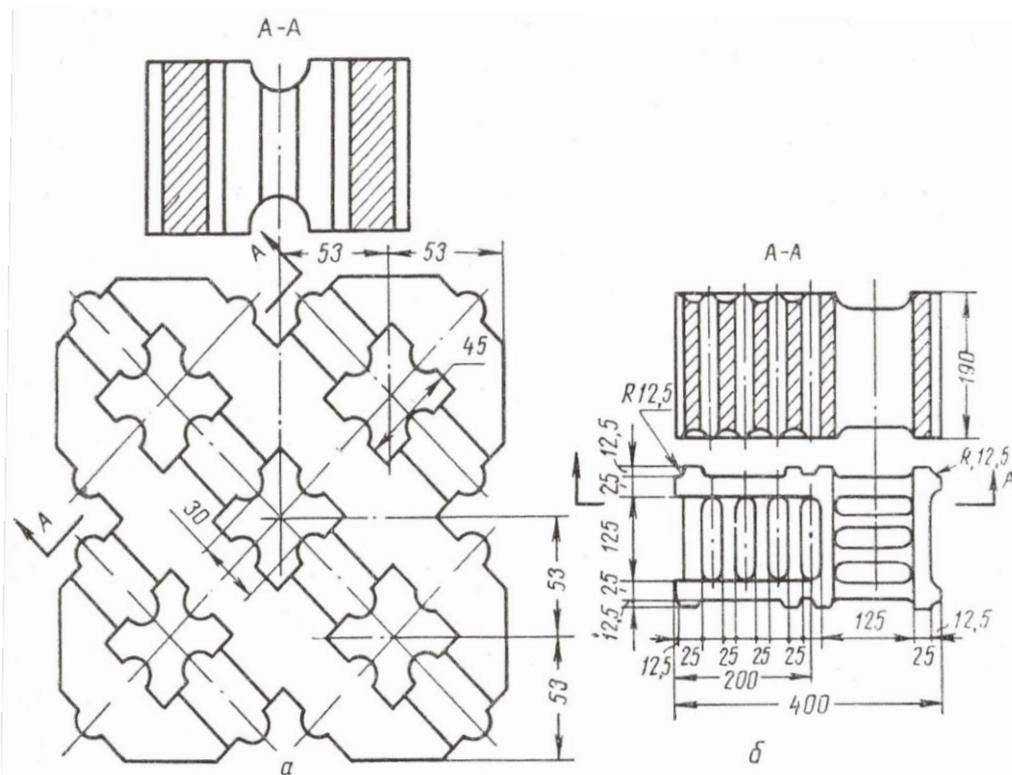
Конструкции насадок ВН из блочного кирпича с горизонтальными проходами: а – с вертикальными полуцилиндрическими выступами; б – со щелевыми каналами
